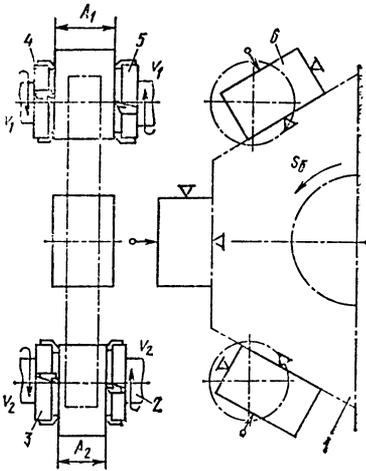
Схема обработки поверхностей на барабанно-фрезерном станке
